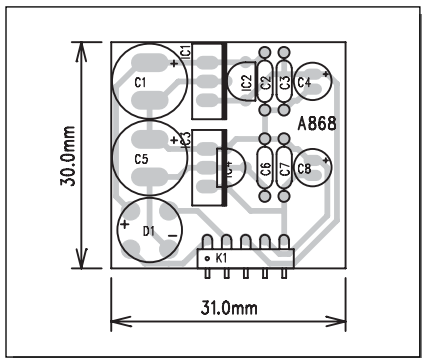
Obrazec desky spojů modulu (A99867)
